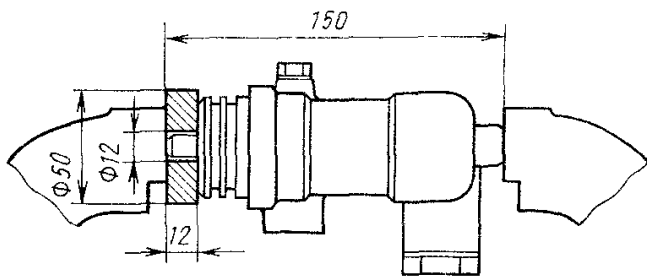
Разборка вторичного корпуса главного тормозного цилиндра
